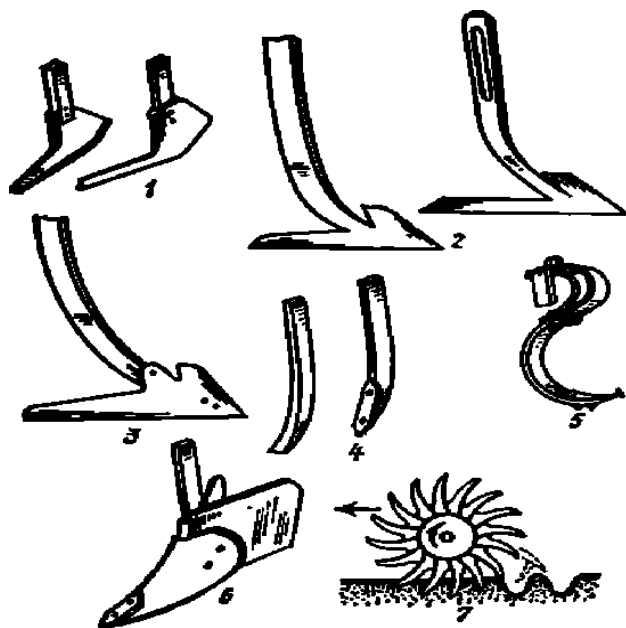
Типы лап культиваторов: 1 – односторонние плоскорежущие; 2 – стрелчатые плоскорежущие; 3 – стрелчатая универсальная; 4 – рыхлительные долотообразные; 5 – рыхлительная на пружинах; 6 – корпус окучника; 7 – игольчатый диск
